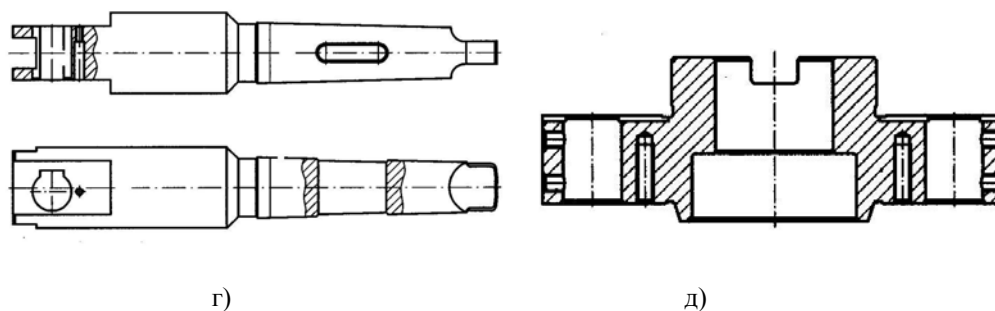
Варианты корпусов блочно-модульных режущих инструментов для:
